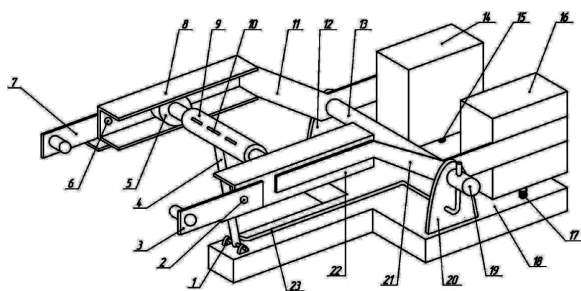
Общий вид системы газодинамической отсечки шлака
